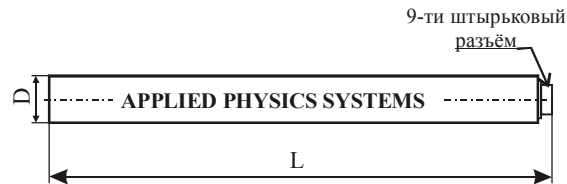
Внешний вид и габаритные размеры датчика типа APS-544
